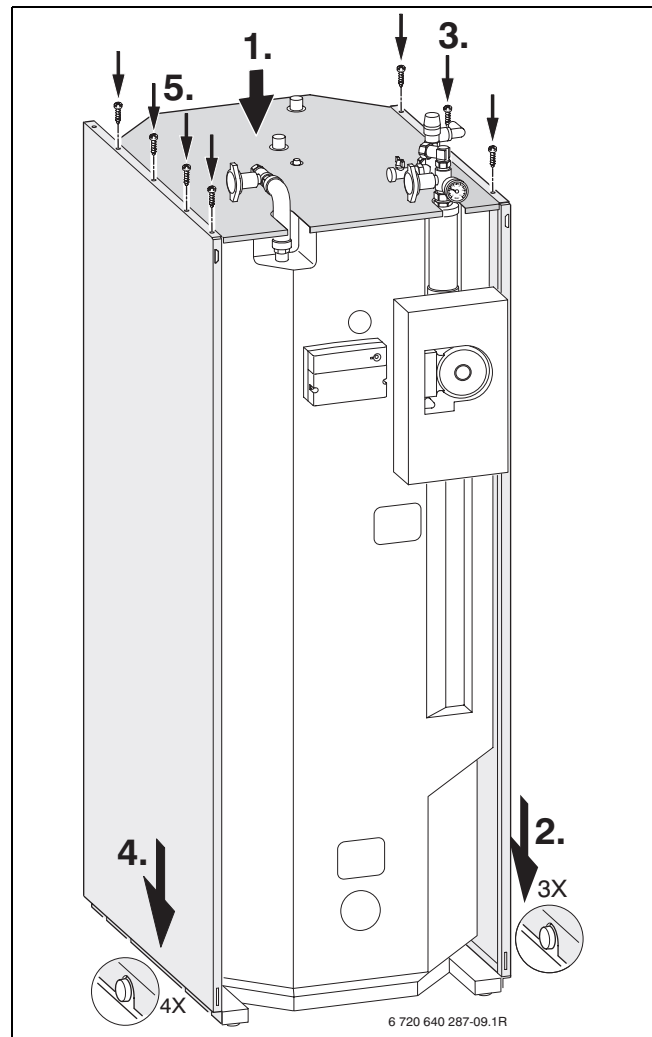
Ejemplo: montaje de las piezas laterales si el acumulador está colocado a la izquierda.
